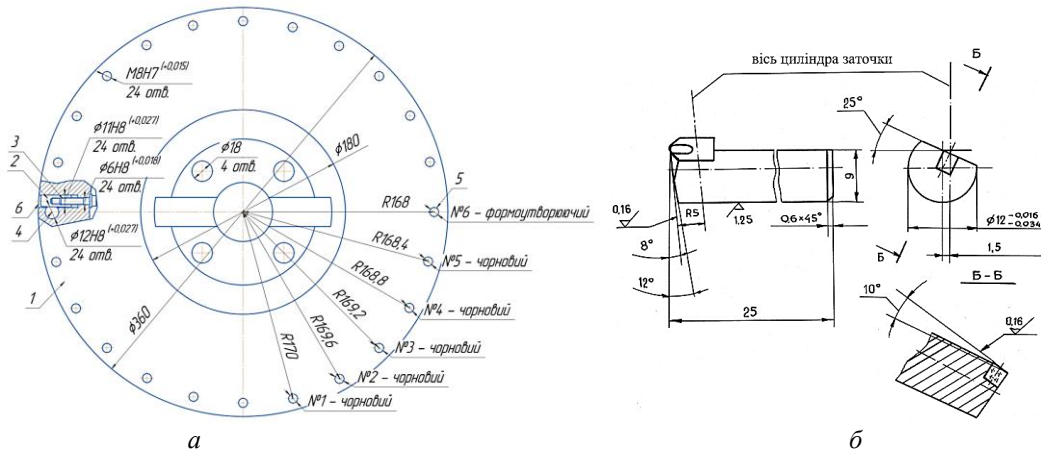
Торцева ступінчаста фреза з 24 різальними елементами: а) торцева ступінчаста фреза, б) конструкція різального елемента [6]
